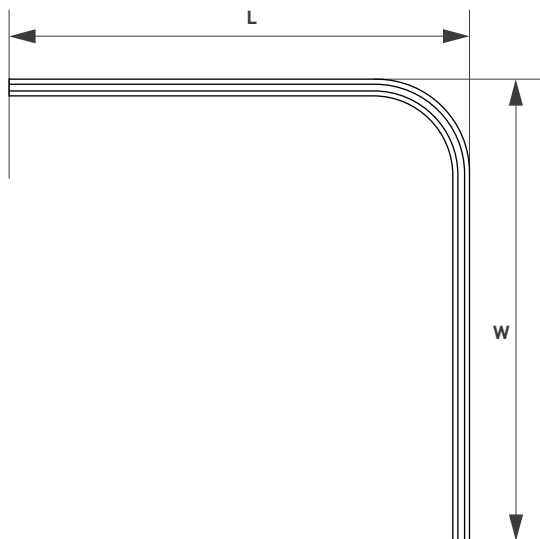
Чертеж и габаритные размеры трека ART-APRIORI-TRACK-ANGLE-A-1722
